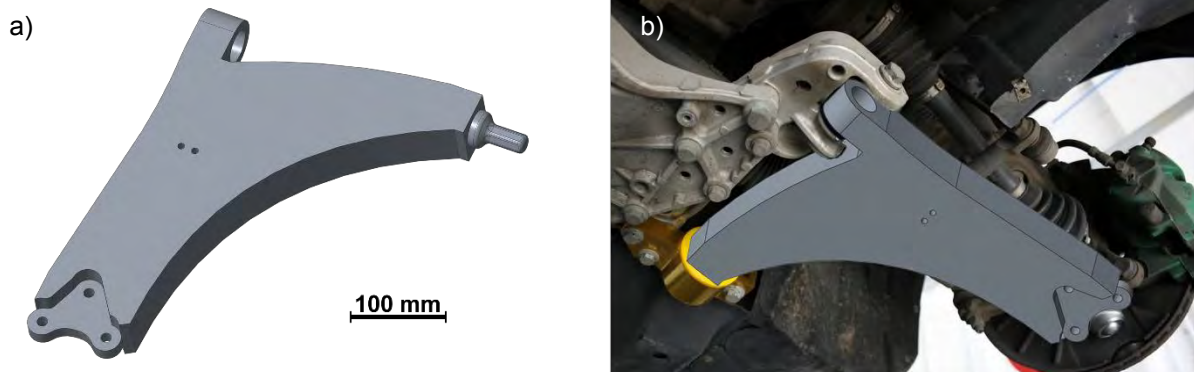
a) CAD-Modell des Querlenker-Bauraums und b) Montage im Fahrzeug
